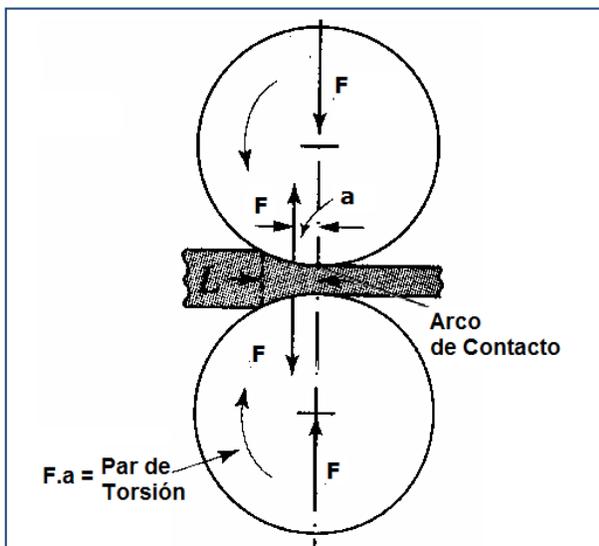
Fuerza perpendicular del rodillo sobre el arco de contacto. (Tomado de *Manufactura, ingeniería y tecnología, Kalpakjian – (Schmid, 4ta ed)*)
